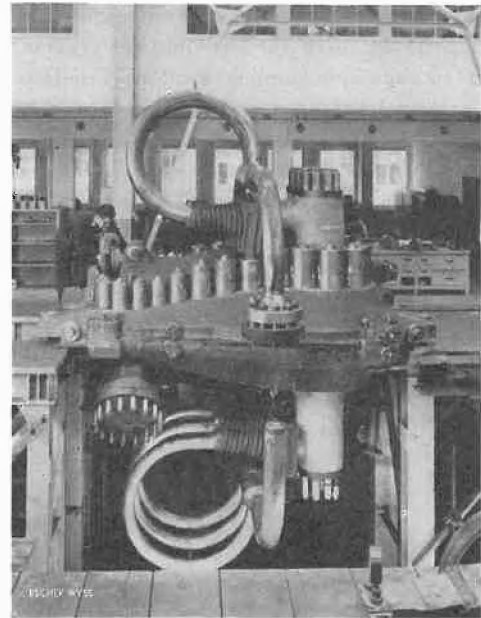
Seitenansicht des geschlossenen HD-Gehäuses wie Abb. 18
